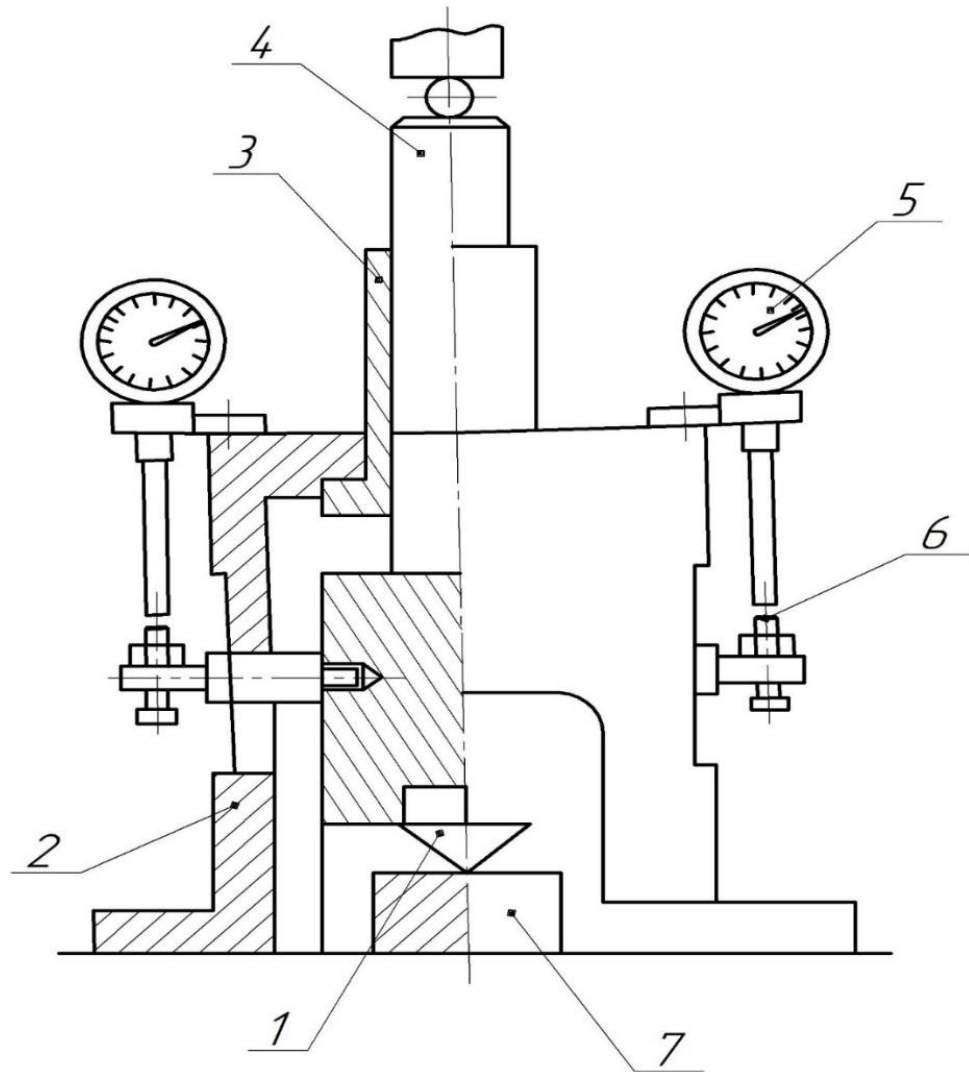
Прилад для вимірювання заглиблення лінійного індентора
